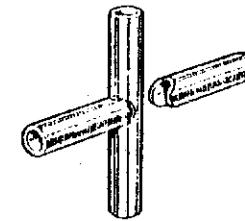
Ajustage de tubes pour soudure d'angle.
